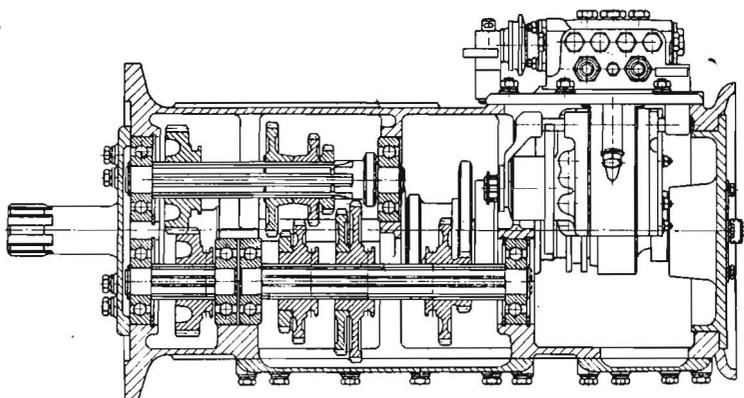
Einbau der Hydraulikpumpe im Getriebe
